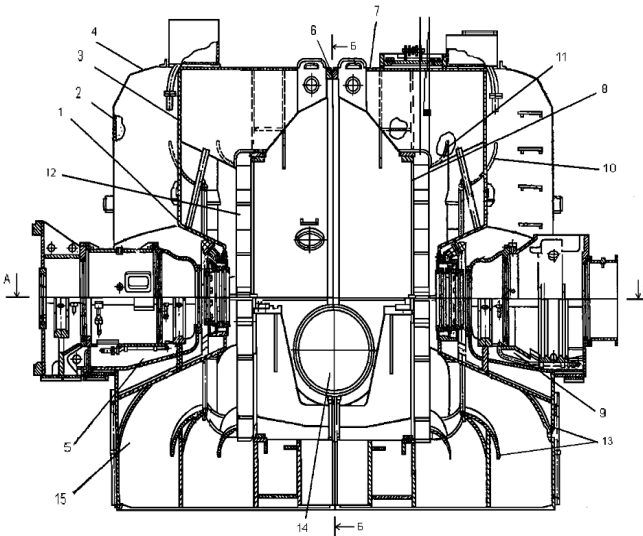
Внешний корпус ЦНД: 1 - конус; 2 - торцевой лист; 3 - лист отверстия; 4 - верхняя часть выхлопного патрубка; 5, 9 - картеры; 6 - вертикальный фланец; 7 - обечайка; 8 - поперечный лист; 10, 12, 13 - направляющие листы; 11 - козырёк; 14 - отверстие; 15 - нижняя часть выхлопного патрубка
